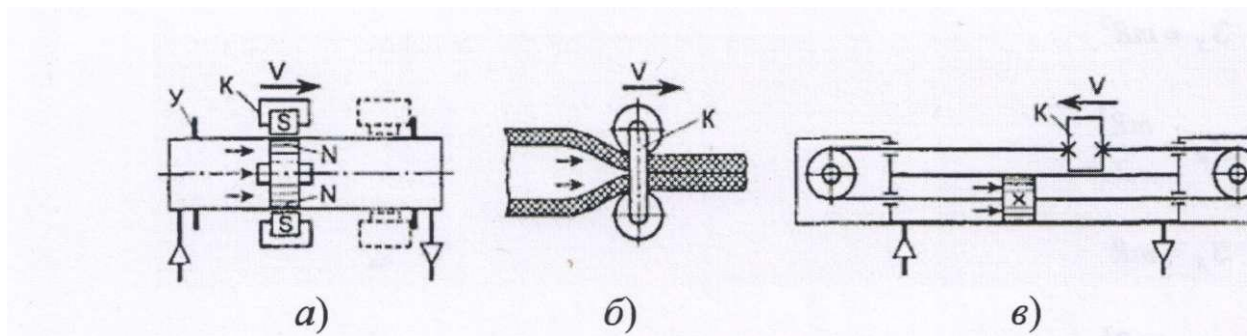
Схемы бесштоковых пневмодвигателей поступательного движения
